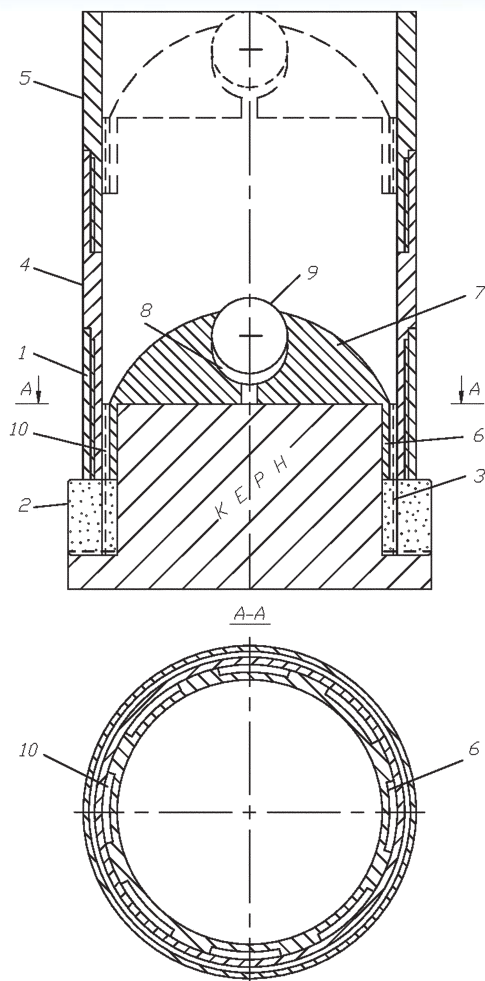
Забойная компоновка с гидрораспределителем и тонкостенной алмазной коронкой: 1 — корпус; 2 — режущая матрица; 3 — промывочные каналы; 4 — расширитель; 5 — колонковая труба; 6 — полый цилиндр; 7 — верхняя полусфера; 8 — приямок; 9 — шаровой поплавок; 10 — проемы
